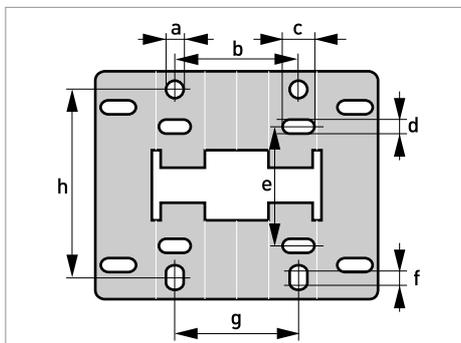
Размеры монтажной пластины корпуса для настенного монтажа
